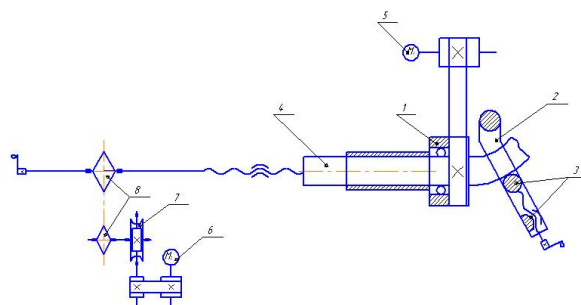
Кинематическая схема станка для гибки труб с обкатыванием
